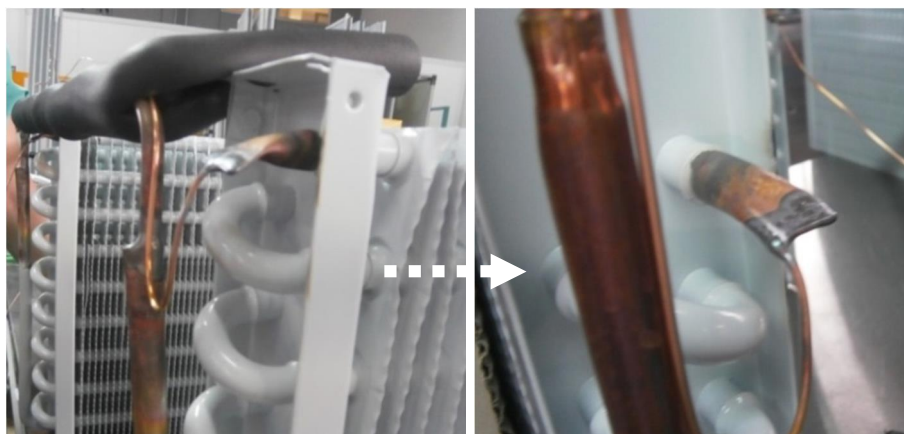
Operação de soldadura capilar - saída do evaporador
